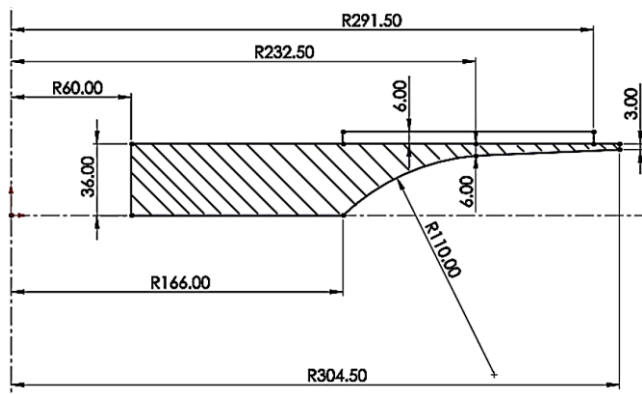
Чертеж модельного колеса с 34-мя лопатками (мм)
